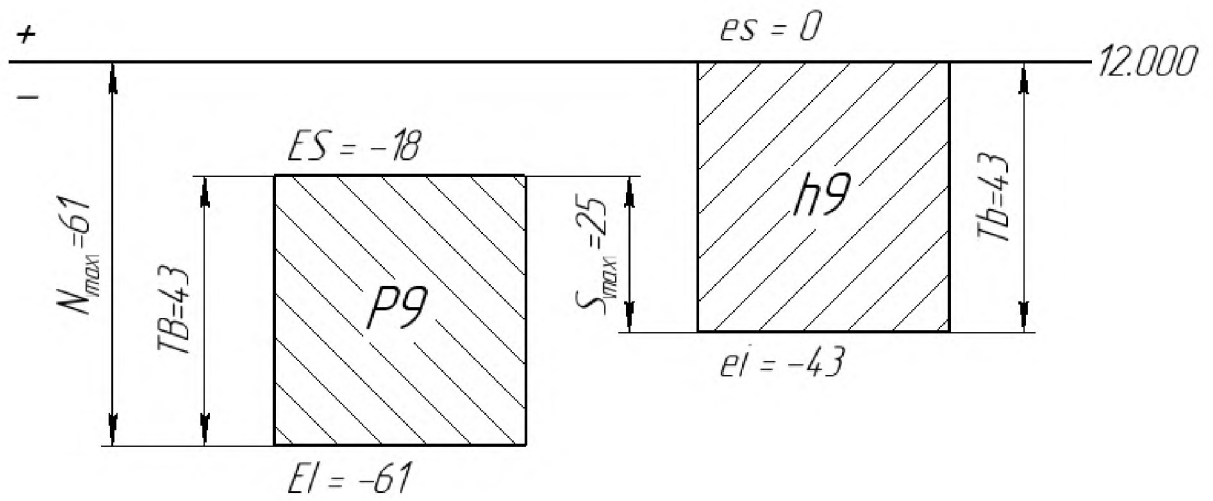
Схема полів допусків з'єднання вал-шпонка
